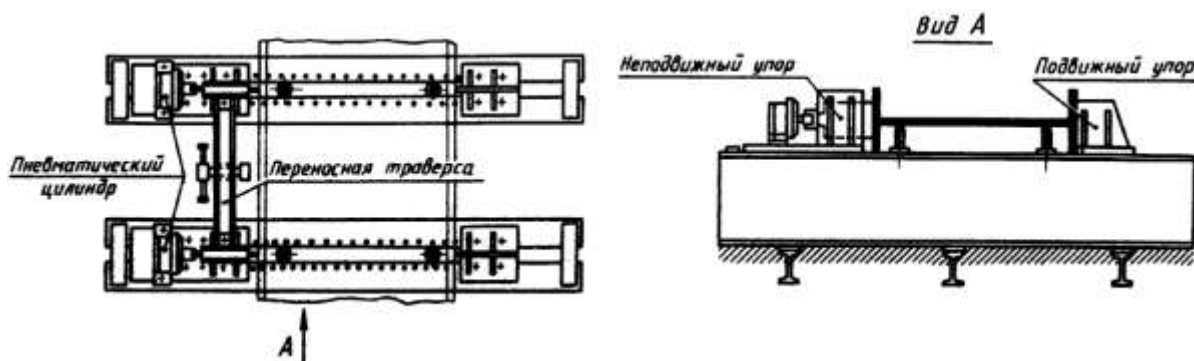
Универсальный сборочный кондуктор с пневматическими прижимами
